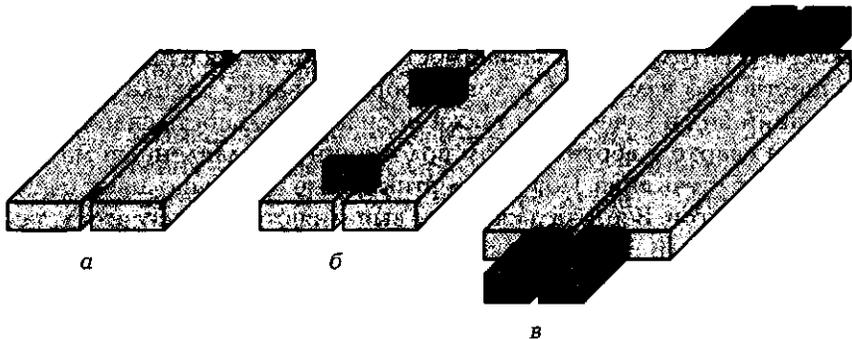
Способы закрепления деталей перед сваркой:
